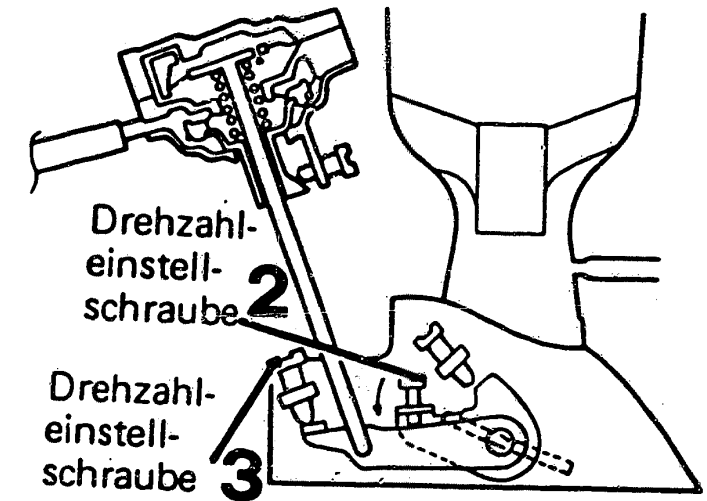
Beim Einstellen der Drosselklappen-Schliessverzögerung ist die Drosselklappe langsam zu schliessen, bis der Hebel die Einstellschraube 2 berührt. Mit der Einstellschraube 3 ist die Drehzahl auf 1800/min zu regulieren.
